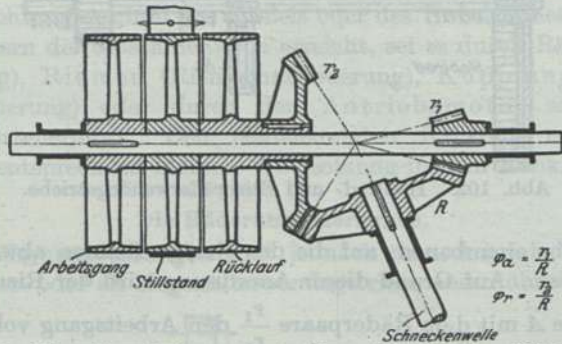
Kegelräderwendegetriebe mit schnellem Rücklauf.
